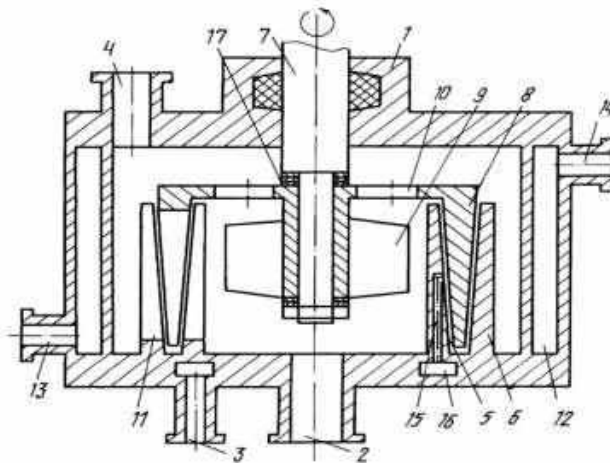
Загальний вигляд роторно-пульсацийного апарата: 1 – корпус; 2, 3 – впускний патрубок; 4 – випускний патрубок; 5, 6 – кільця статора; 7 – вал; 8 – ротор; 9 – лопаті; 10 – отвори; 11 – коаксіальні конуси з прорізами; 12 – сорочка; 13, 14 – штуцери; 15 – канали; 16 – камера; 17 – регулювальна шайба
